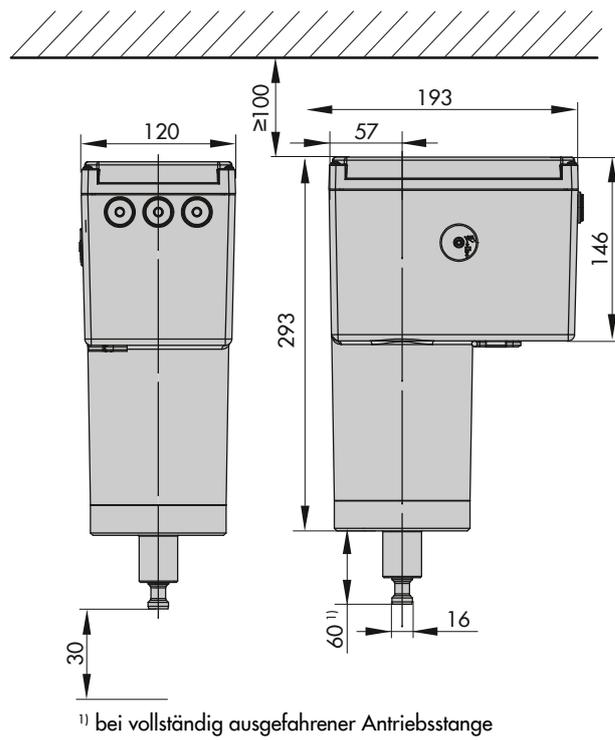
Maße in mm · Typ 3374-35, Ausführung Form A
